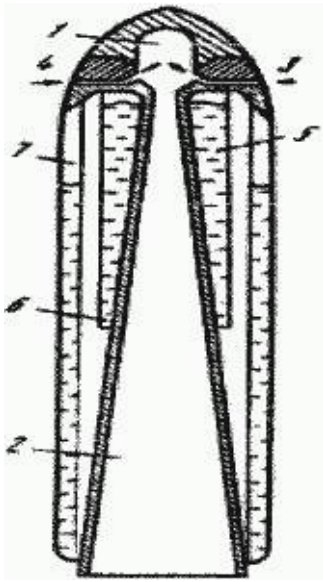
Схема охлаждения двигателя ракеты АРО №3
